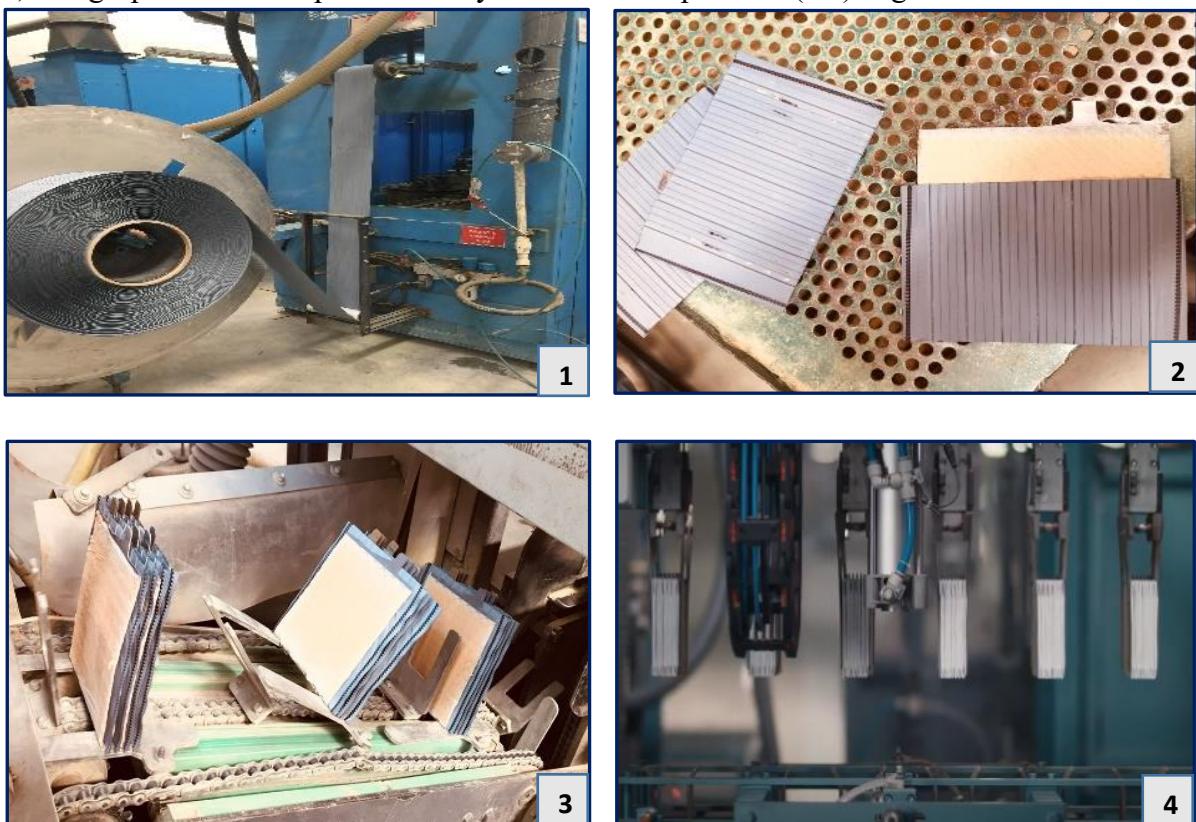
Montaj Hatti İş Aşılış Şeması
